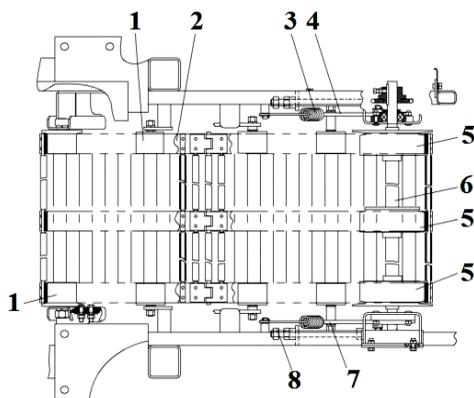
Второй сепарирующий элеватор: 1 – ролики поддерживающие; 2 – ремень; 3 – пружина; 4, 7 – кронштейны; 5 – колеса ведущие; 6 – вал приводной; 8 – шпилька
